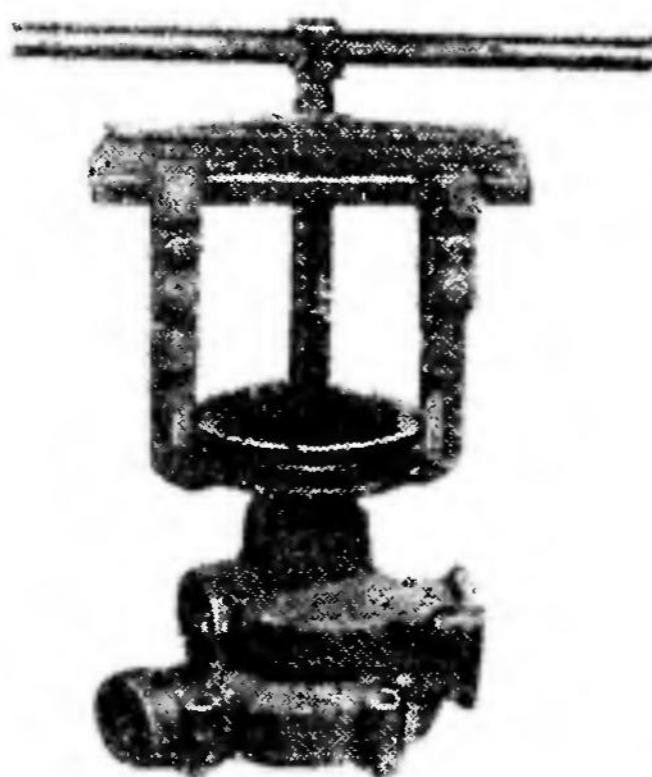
Снятие шкива съемником зубчатых колес и противовесов коленчатого вала
